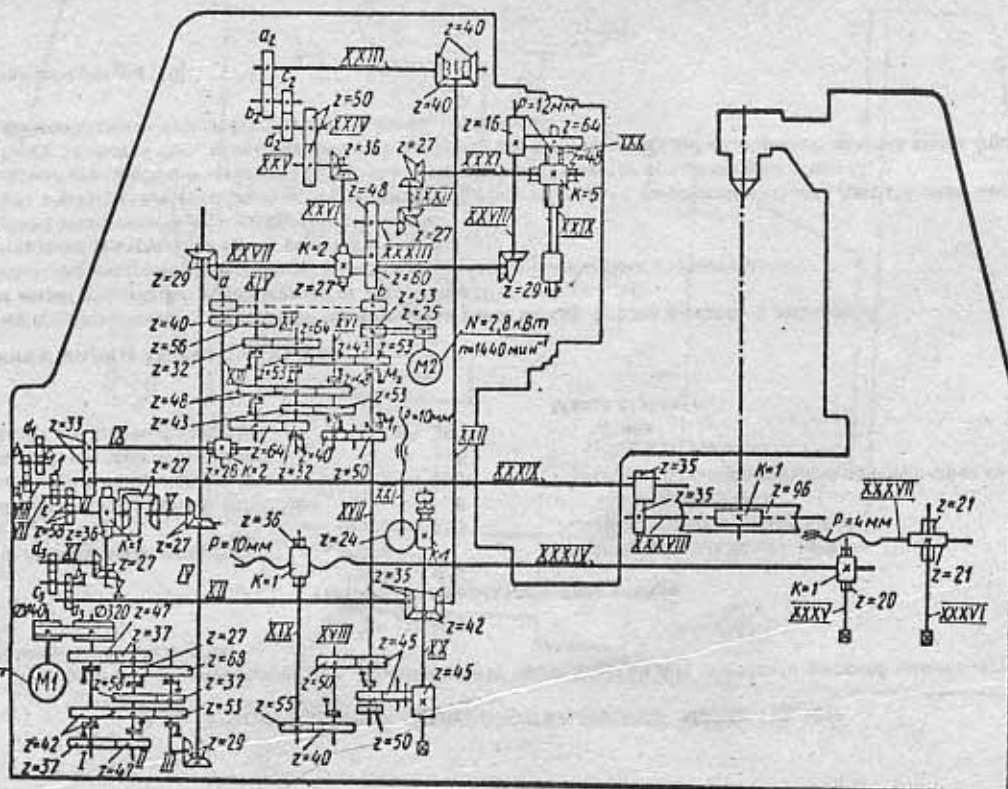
Кинематическая схема зубофрезерного полуавтомата мод. 5К324
